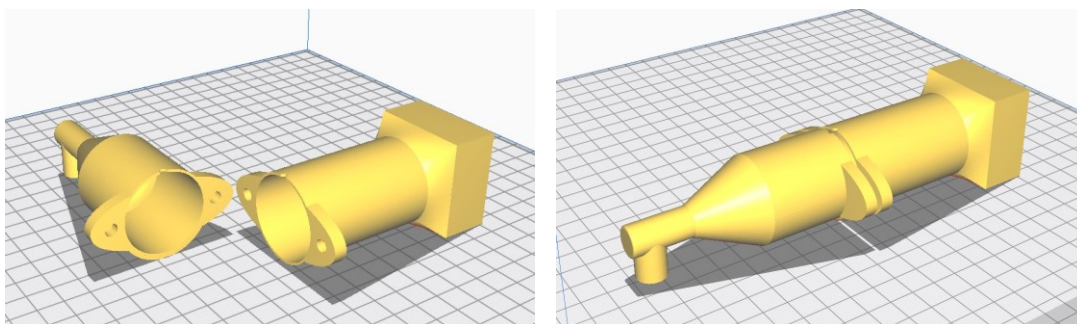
Getestetes Design eines Duftsammlers, hergestellt mit einem 3D-Drucker
